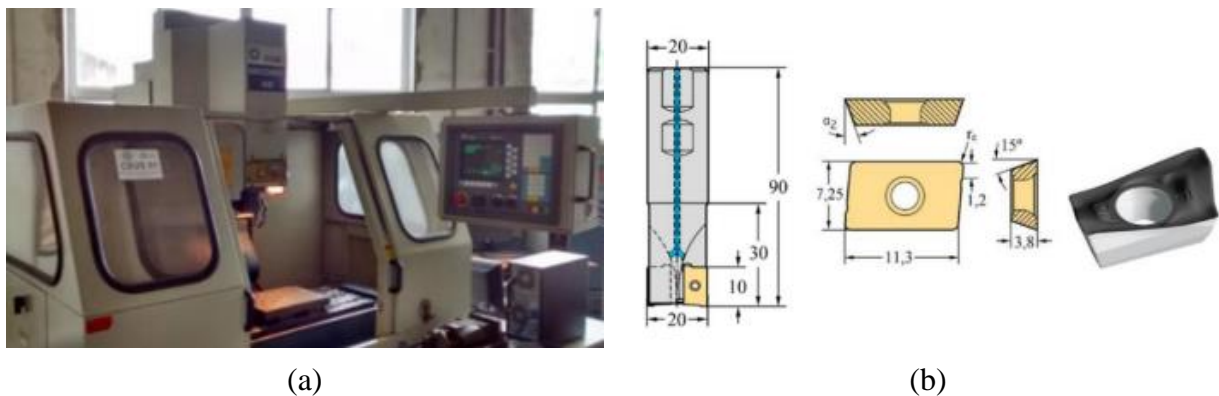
(a) Centro de Usinagem ROMI Discovery 308; (b) Geometria da ferramenta de corte [Walter Tools, 2012].
